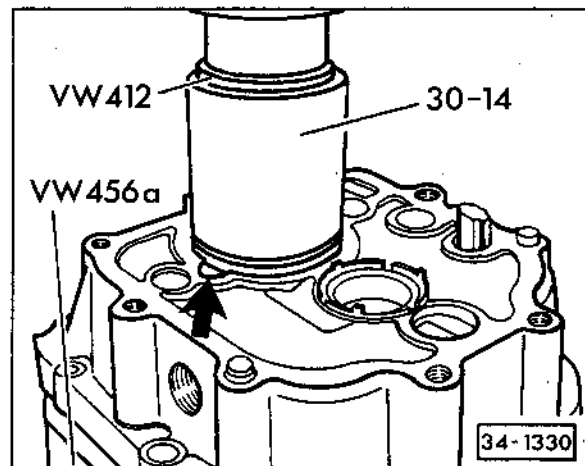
Rillenkugellager bis Anschlag in Lagerschild einpressen
